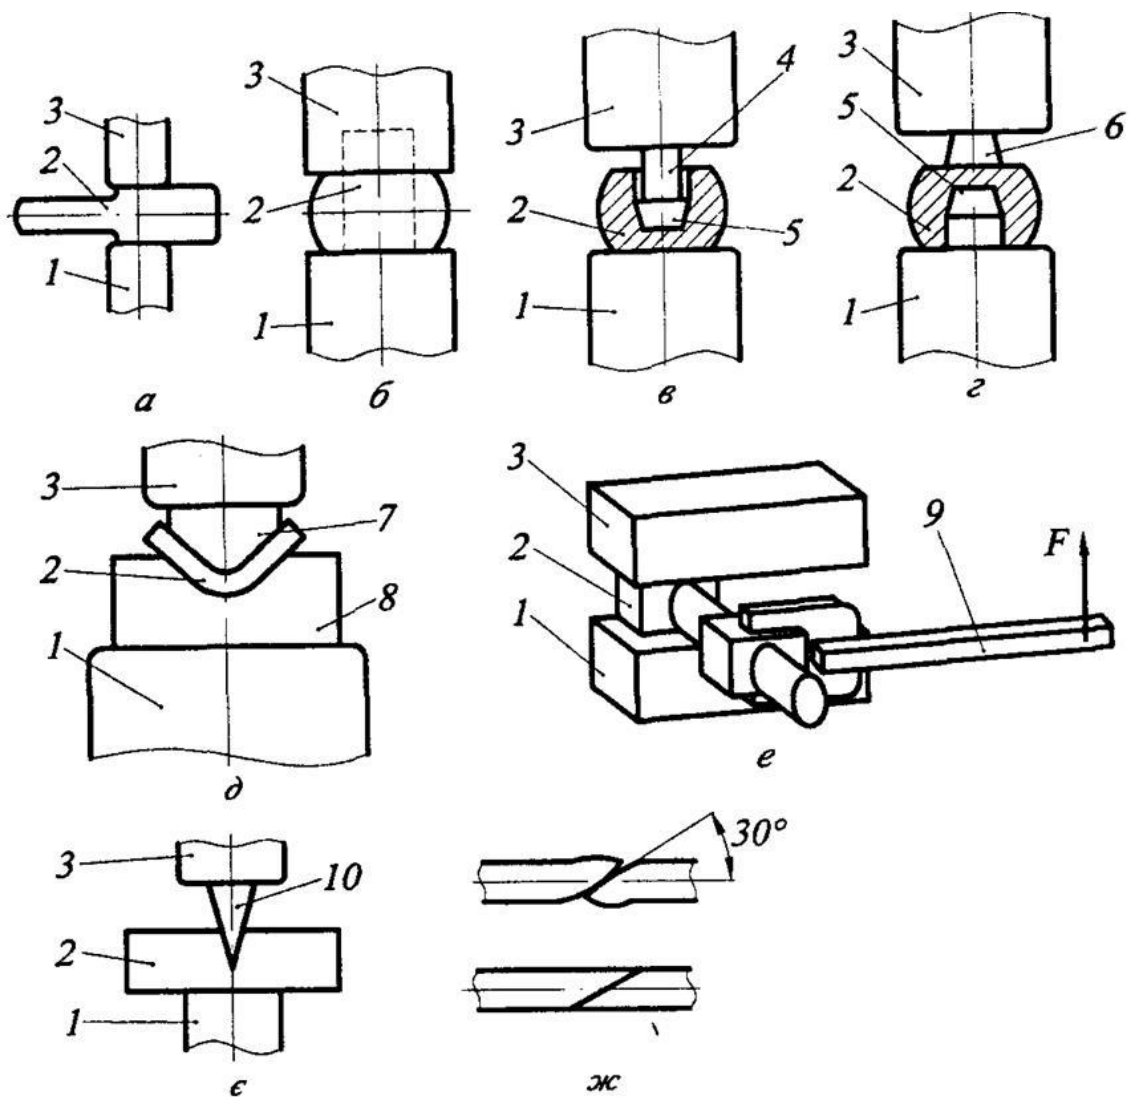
Видовження (а); сплющування (б); пробивання (в, г); гнуття (д); кручення (е); рубання (е); ковальське зварювання (ж): 1, 3 – нижній і верхній ударник; 2 – заготовка; 4 – надставка; 5, 6 – прошивень; 7, 8 – половини штампа; 9 – вилка; 10 – сокира; F – сила.
